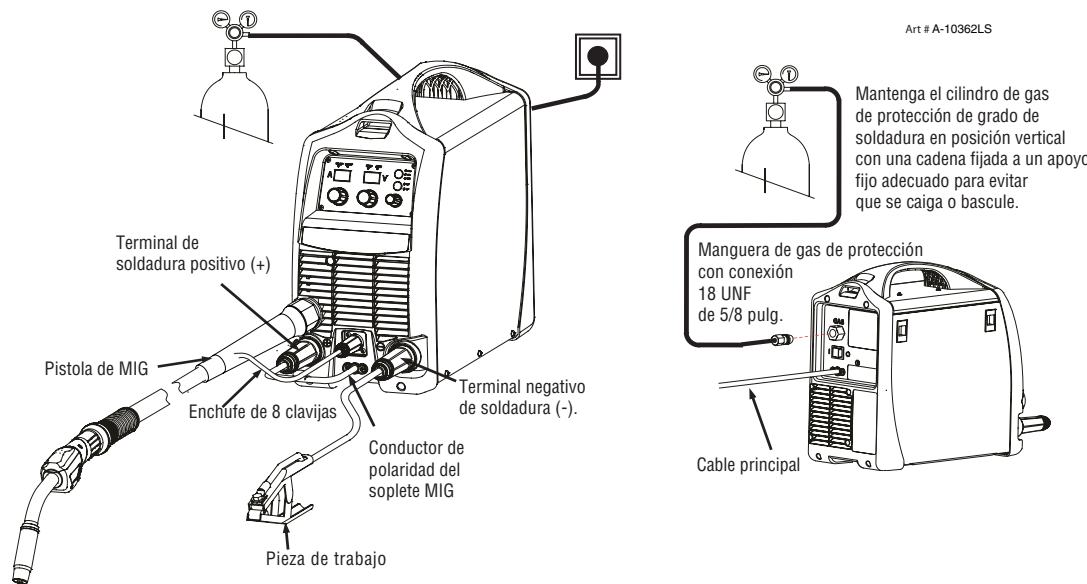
Configuración de la soldadura MIG (GMAW) con el alambre MIG protegido con gas
